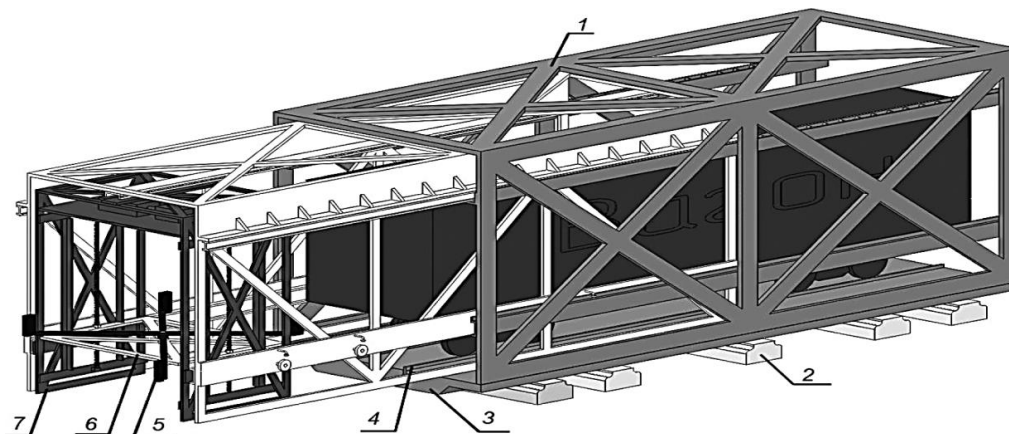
Схема конструкції роботизованого транспортного агрегату для переміщення вагонів між позиціями гнучкого виробництва: 1 – телескопічний портал; 2 – приводні візки; 3 – горизонтальна платформа; 4 – дільниця рейкової колії; 5 – електромеханічний захват; 6 – вертикальна підйомна каретка; 7 – пересувний внутрішній портал
